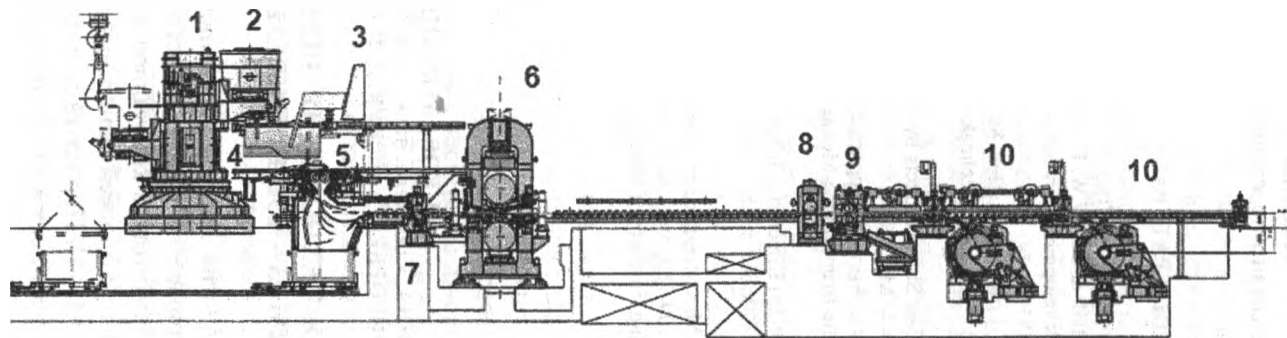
Схема литейно-прокатного модуля Castrip: 1 – поворотное устройство; 2 – ковш; 3 – плазменная дуга (для контроля температуры); 4 – промежуточный ковш; 5 – валки-кристаллизаторы; 6 – прокатный стан; 7 – поджимающие ролики; 9 – ножницы; 10 – зона намотки
